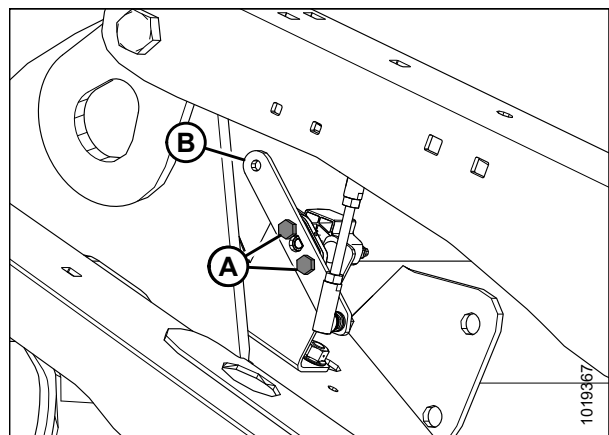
Haspelhöhsensor – Rechter Haspelarm
